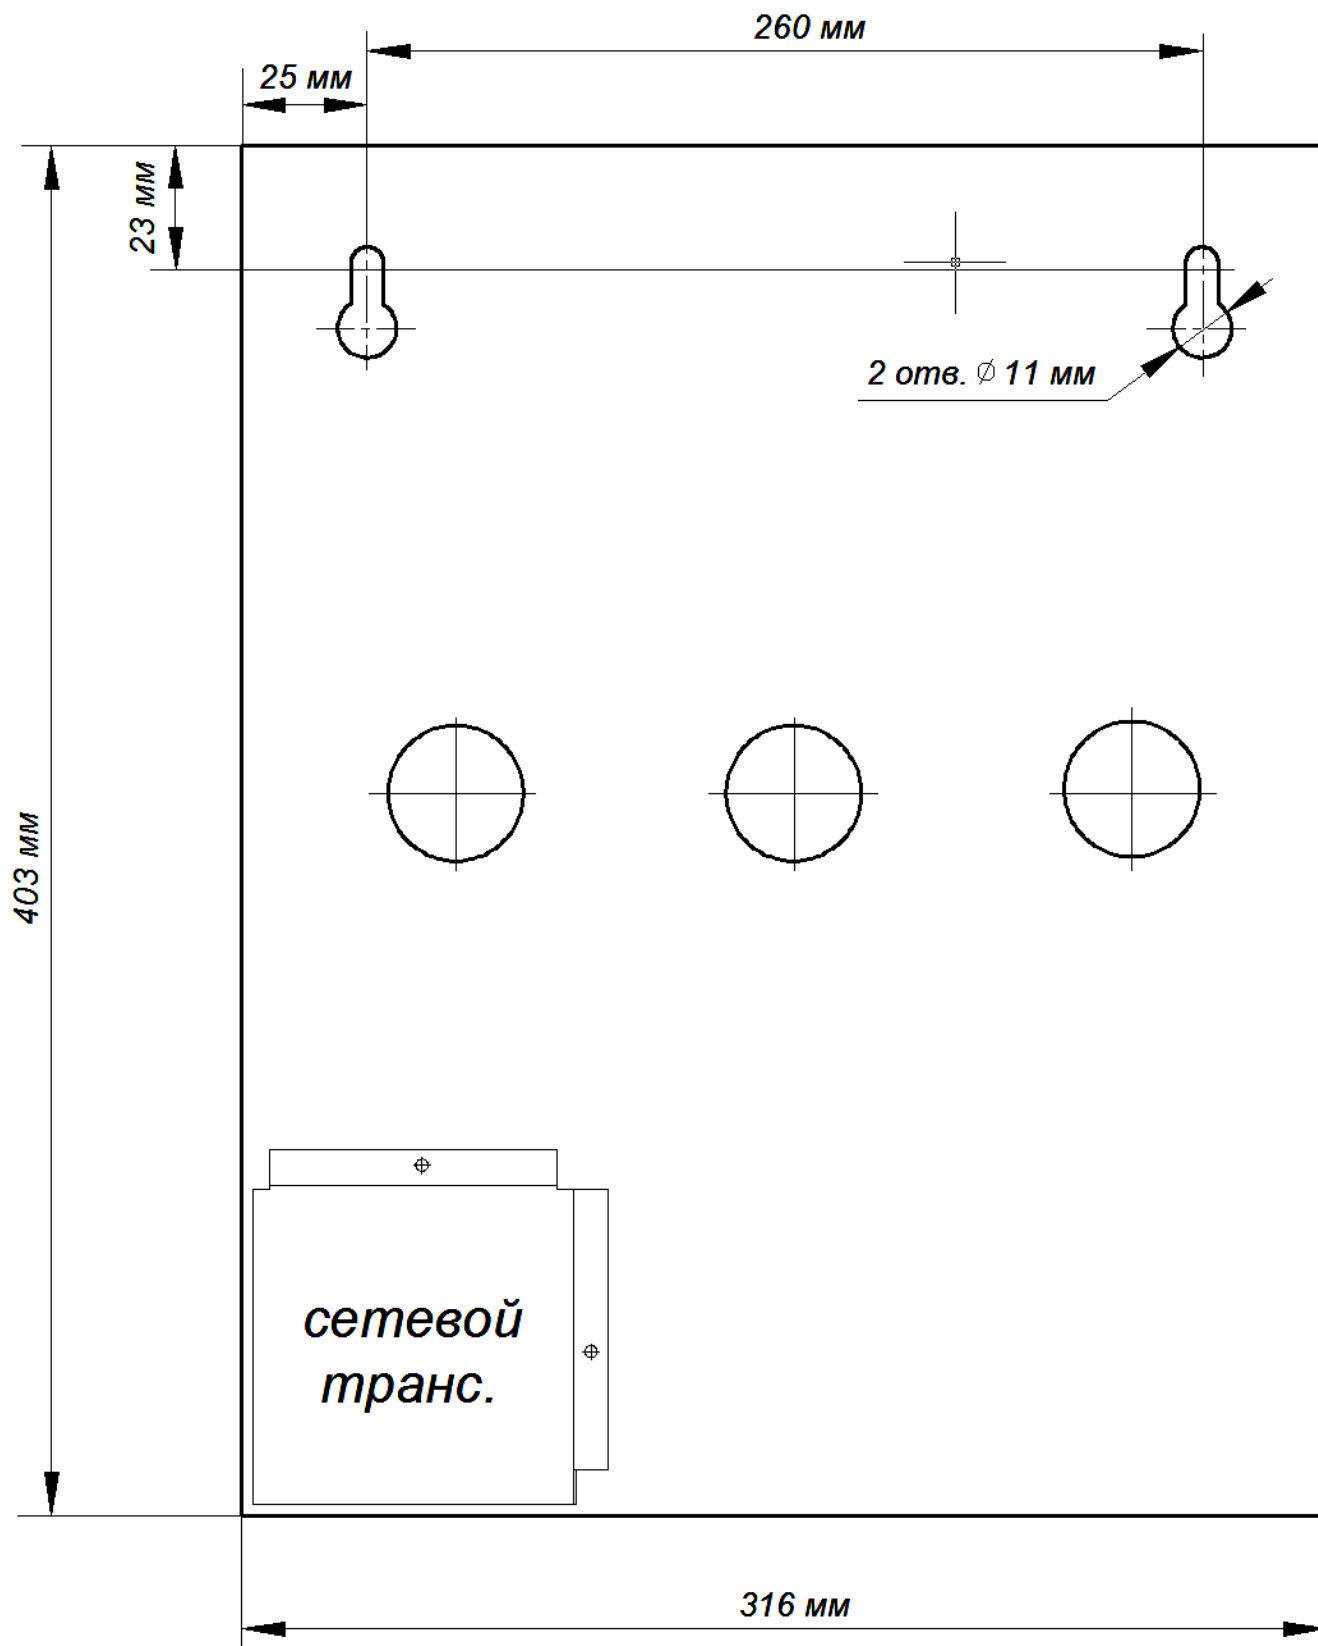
Установочный чертеж прибора «А16-512» (корпус выпускается начиная с 2012 года)
